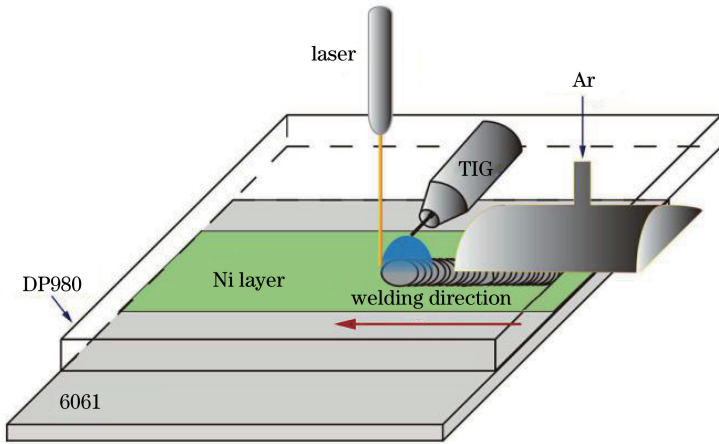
6061 铝合金/DP980 高强钢激光诱导电弧复合焊接示意图
